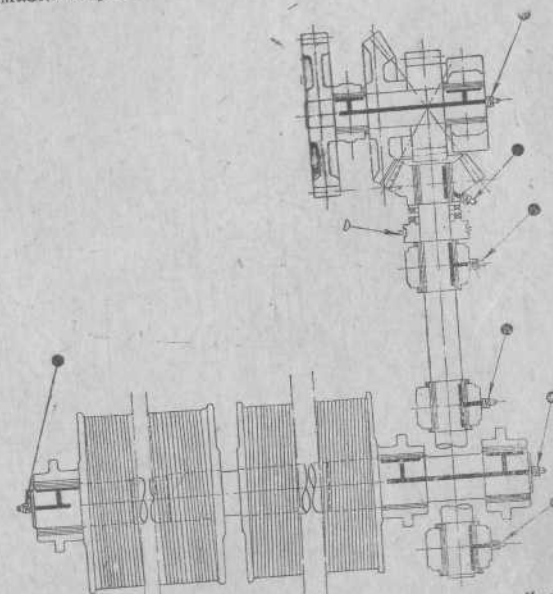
Схема смазки промежуточного вала главной передачи и механизма подъема стрелы
